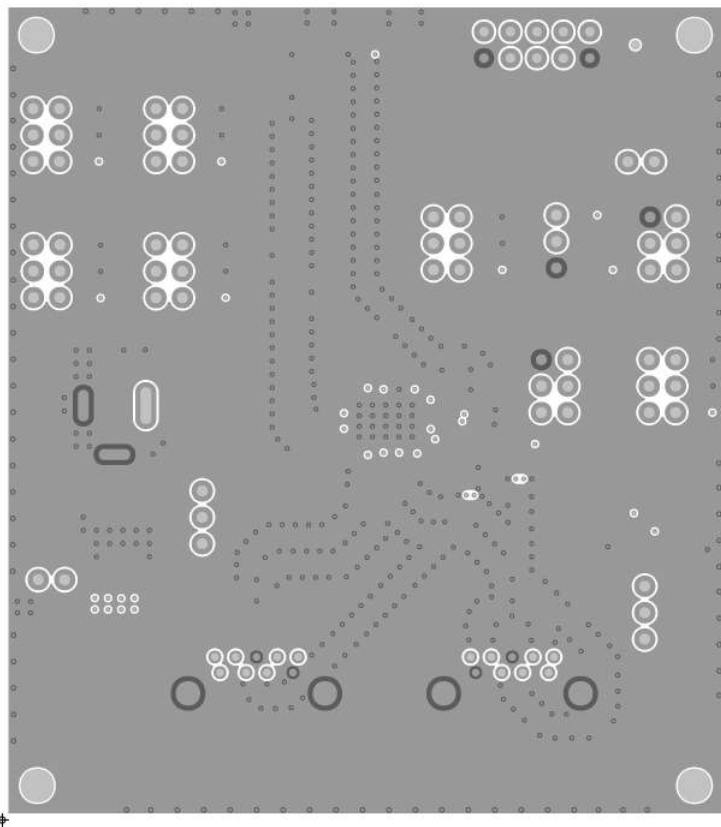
TUSB521Q1-EVM PCB 第 5 层 ( 接地 )
